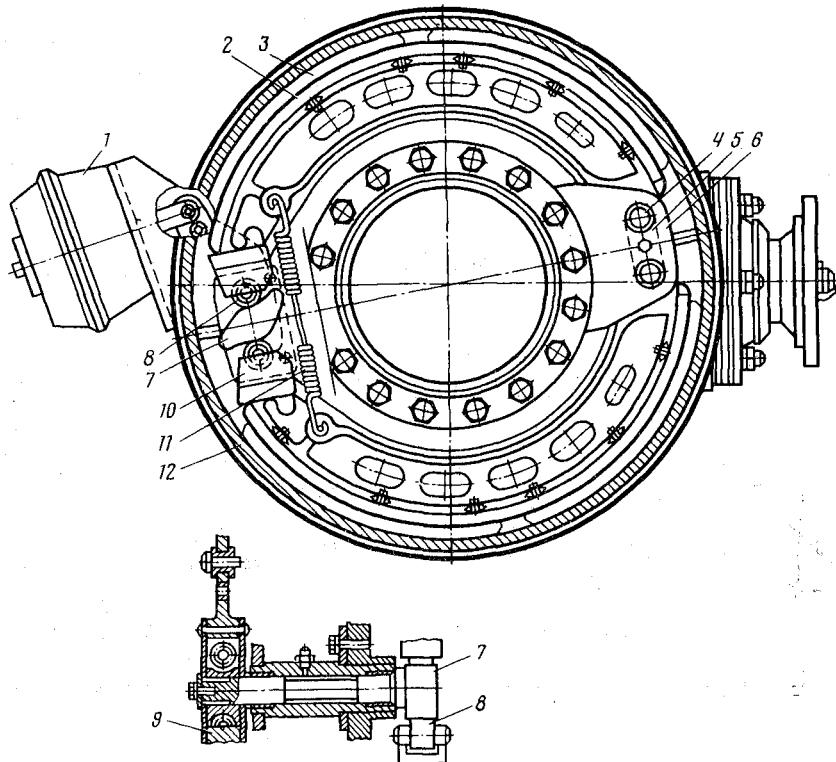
Схема работы колесного тормоза скрепера ДЗ-11П
